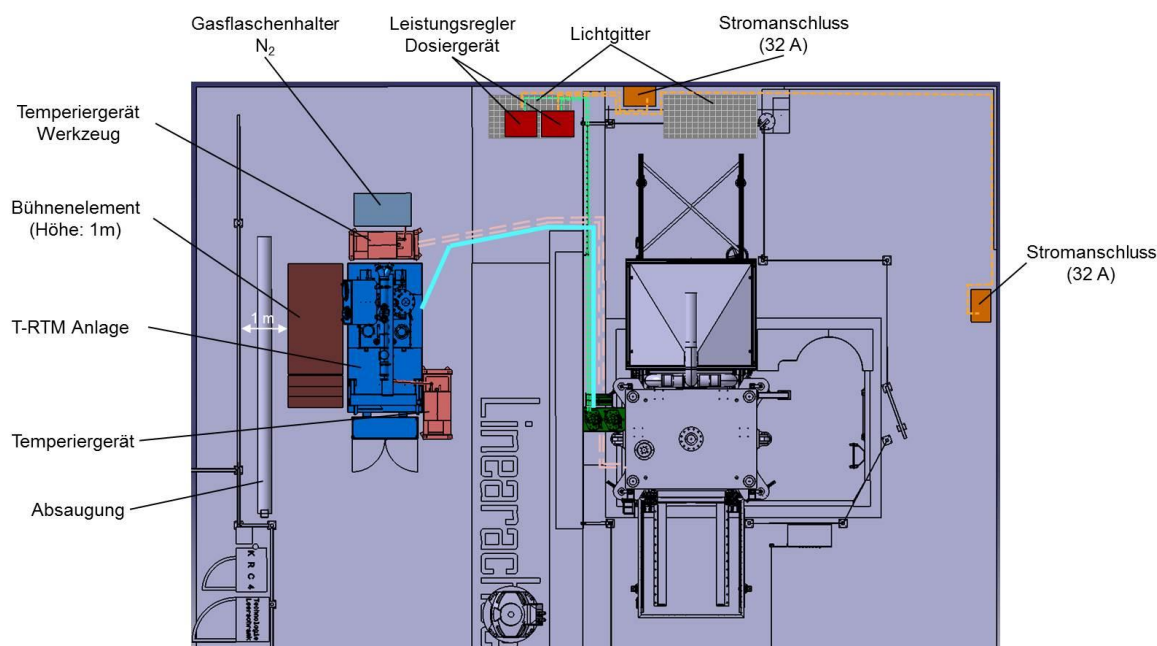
Anlagenlayout für Versuchsreihe mit Plattenwerkzeug
